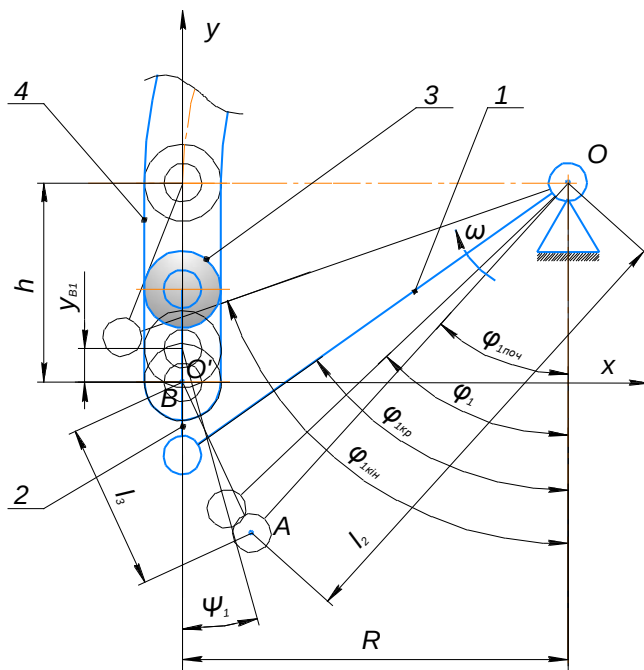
Розрахункова схема для визначення величини переміщення шарніра головки укладальника пляшок на першому етапі: 1 — кривошип; 2 — шатун; 3 — шарнір кріплення захватної головки; 4 — напрямна
